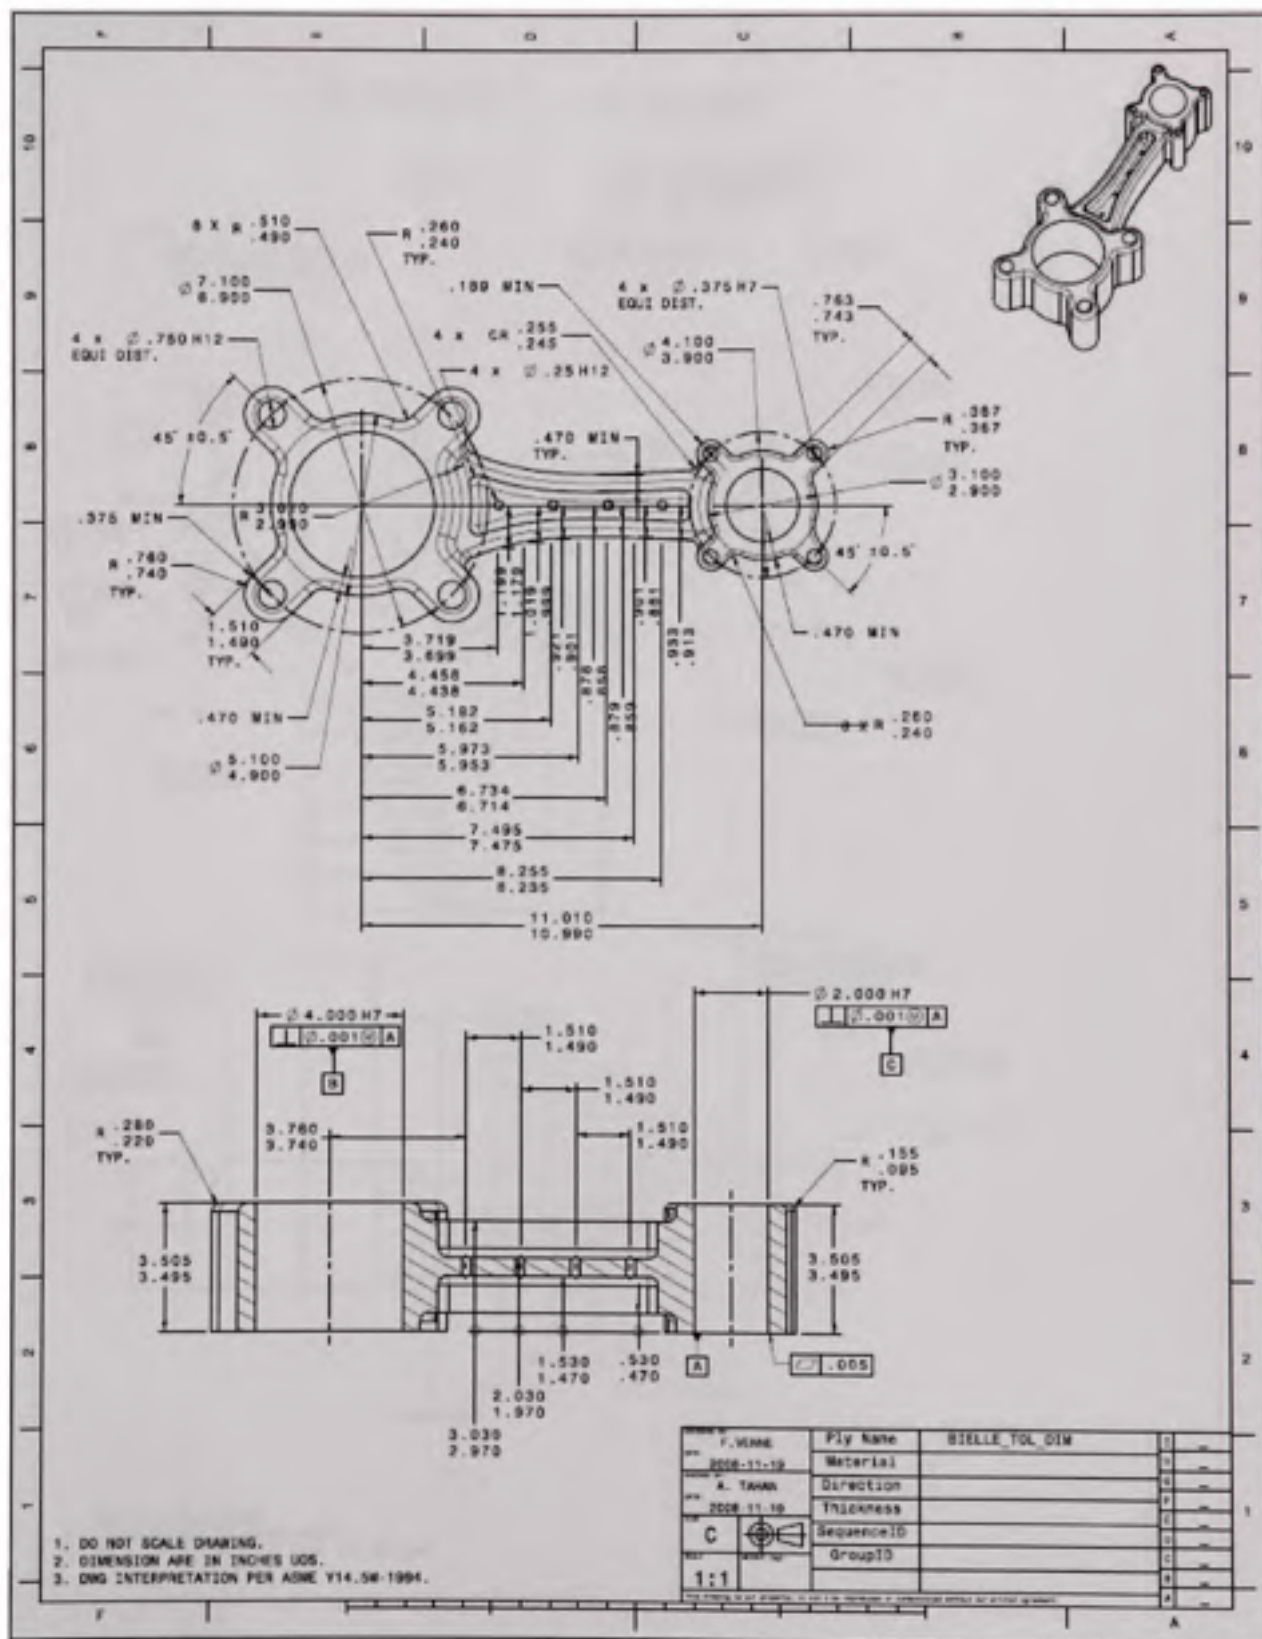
Dessin dimensionnement traditionnel dimensionnel.
